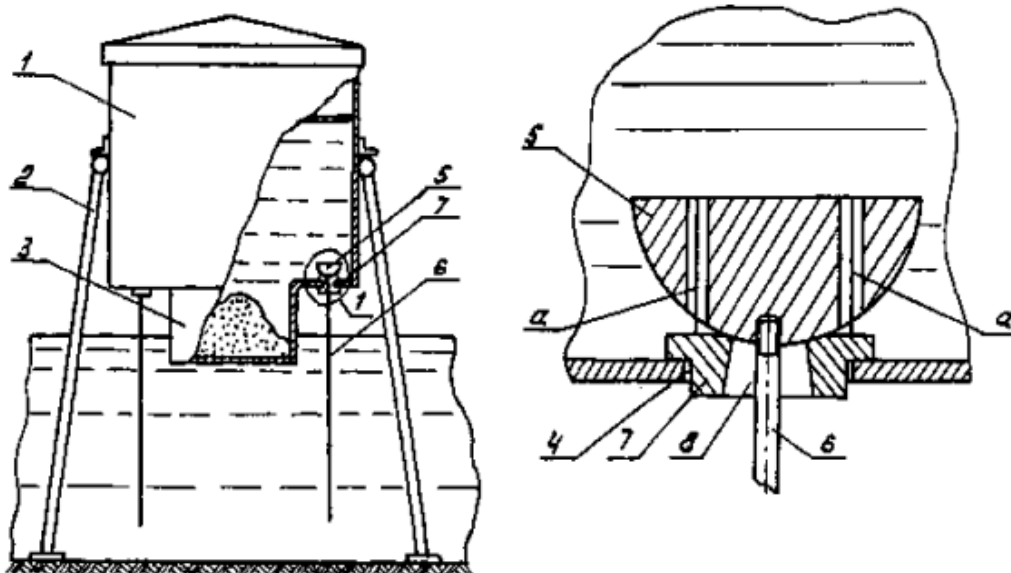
Устройство для выдачи извести. 1- бункер; 2- опоры; 3-приемник для извести; 4- резиновая прокладка; 5- полусфера; 6- маятник; 7- шайба; 8-отверстие.
